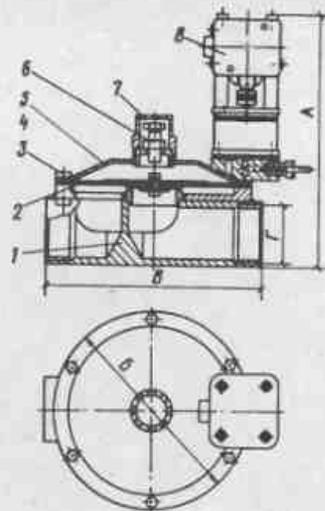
Общий вид конструкции клапанов КГ-20, КГ-40, КГ-70
